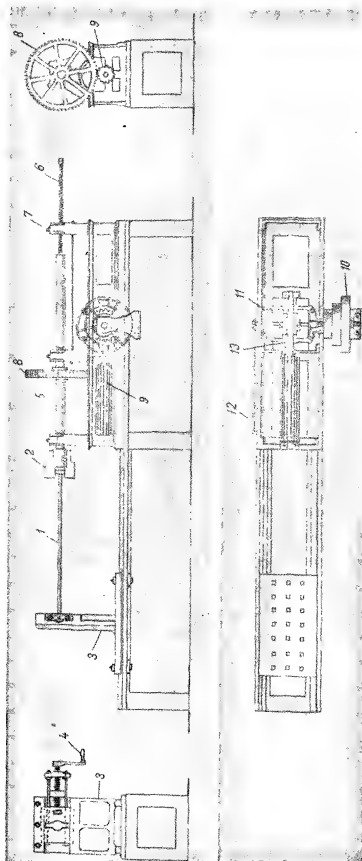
Винторезный станок Луганского завода. 1829 г. Заводской чертеж.
